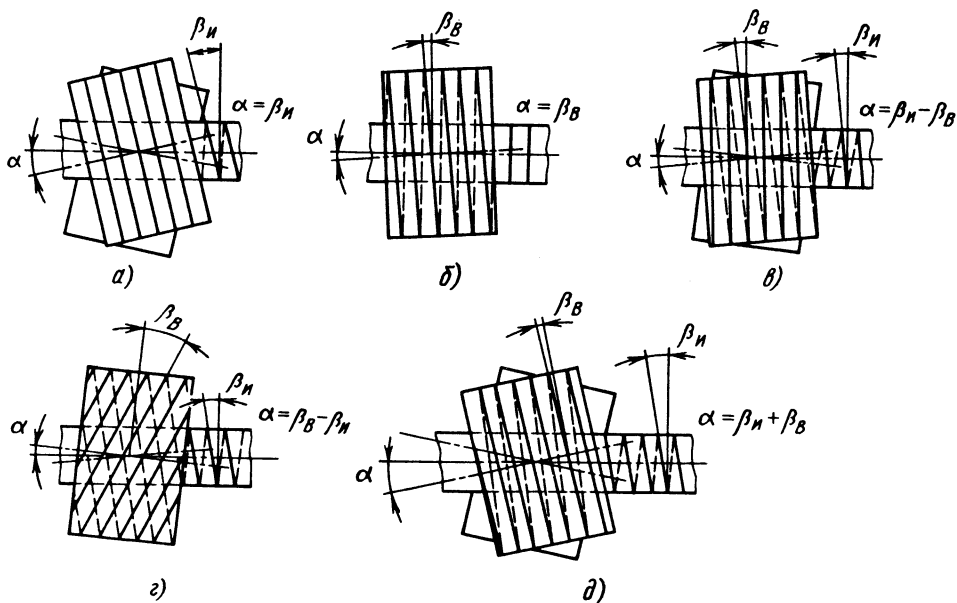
Схемы поперечно-винтовой прокатки в кольцевых и винтовых калибрах
